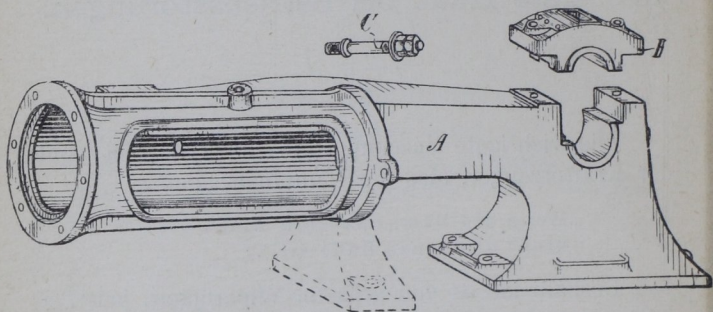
Bajonettrahmen. A Rahmen, B Lagerdeckel, C Deckelschraube.
